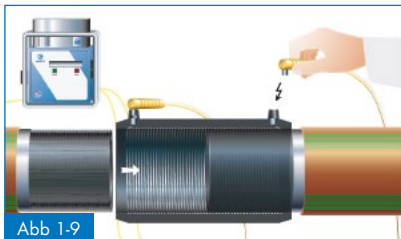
Verschweißen gemäß DVS 2207, Teil 1
